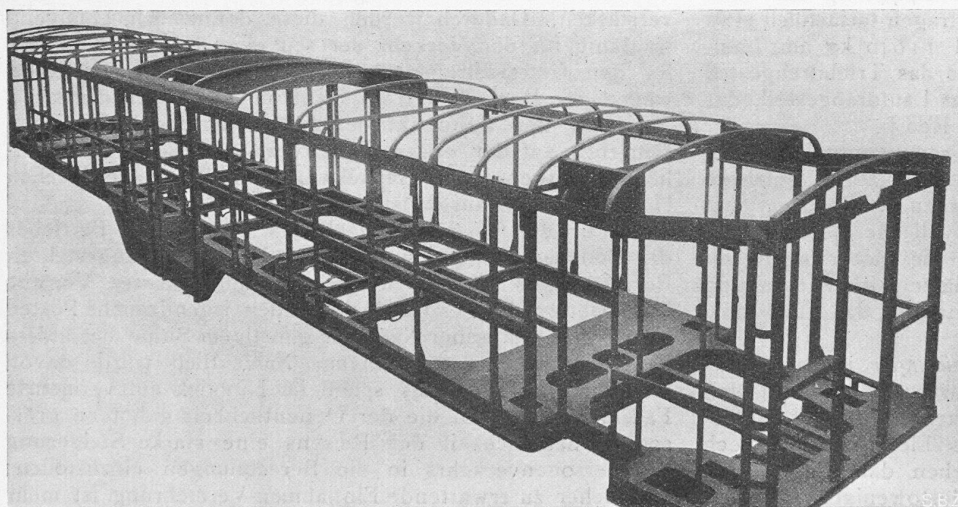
Stahlgerippe des Kastens der Motorwagen. Schweiz. Industrie-Gesellschaft Neuhausen.
